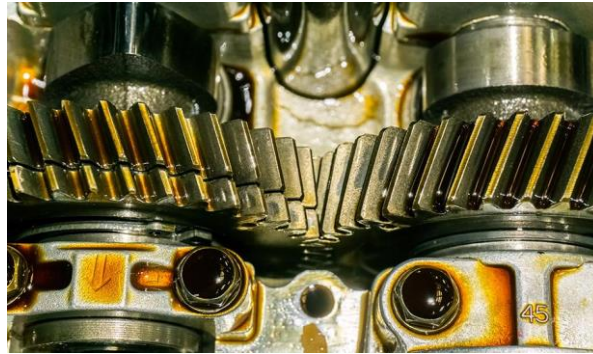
Conjunto de engrenagens lubrificadas por chapinagem ou salpicos [30].
